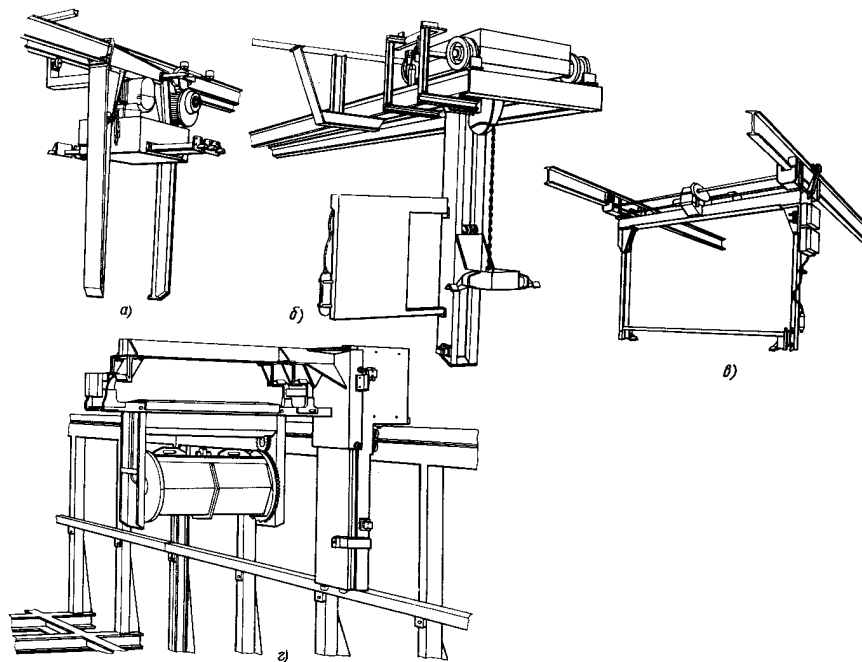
Автооператоры фирмы Blasberg: а – тельферный с раздвижными грузозахватами; б – подвесной тележечный с консольным грузозахватом; в – мостовой; г – консольный.
